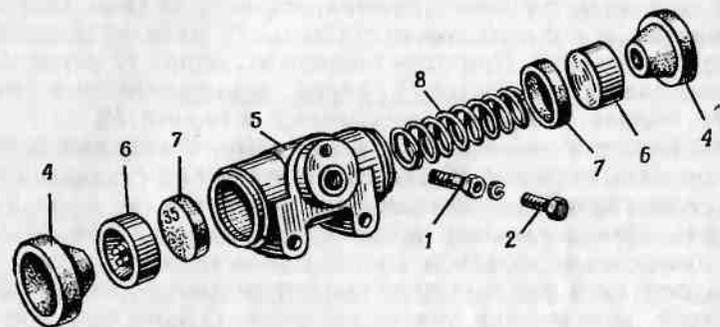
Детали рабочего цилиндра (обозначение деталей то же, что на рис. 137)
